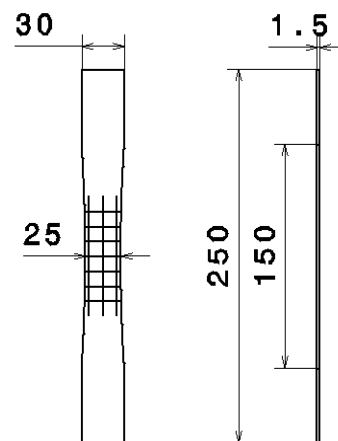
Géométrie des éprouvettes sens trame et chaîne
